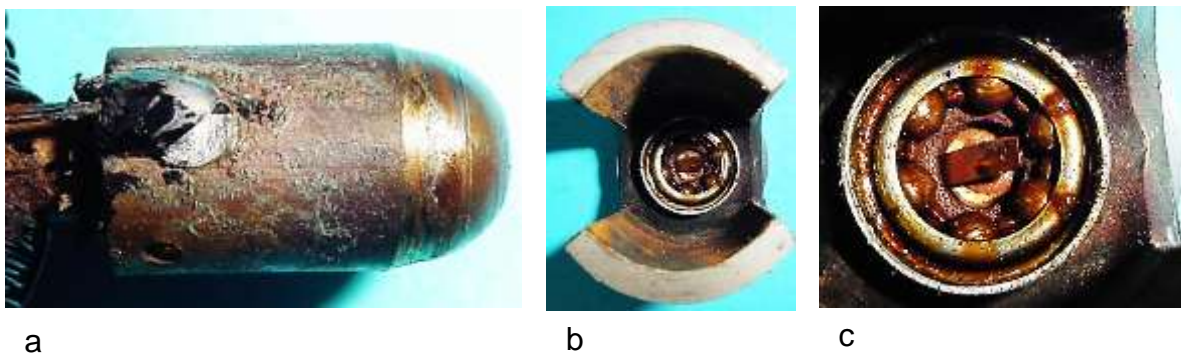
Unteres Kugellager: a) Eingepresste 10 mm Kugel am Wellenende, b) Position des Kugellagers auf dem Magnetjoch, c) Kugellager mit Kontaktfeder
